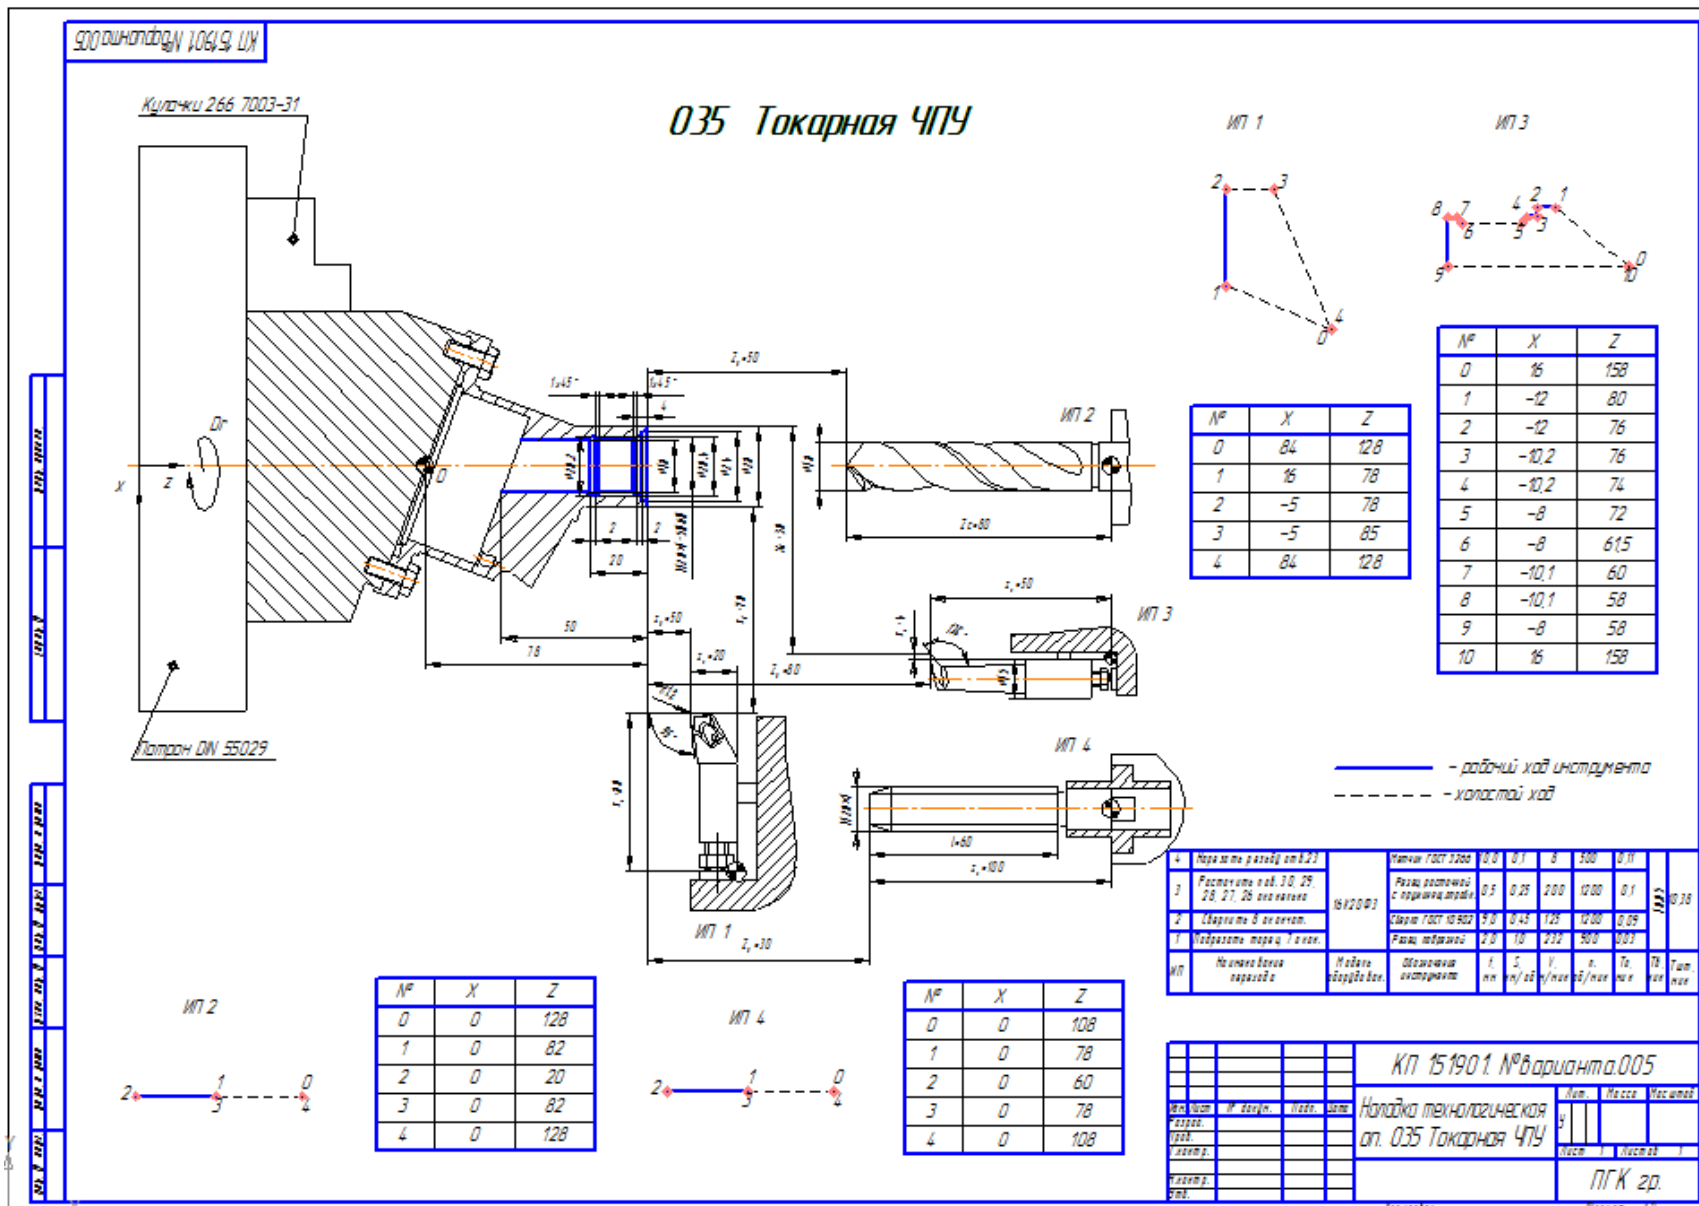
Карта наладки обработки детали «Крышка».
